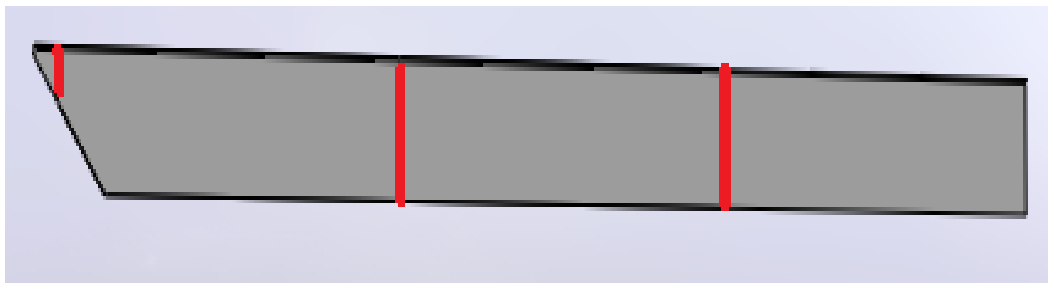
Matriz soldado con conjunto frente intermedio y superior.
